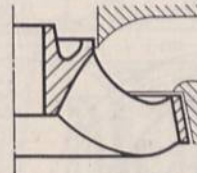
Francisturbinenrad für hohe Laufgeschwindigkeit.
